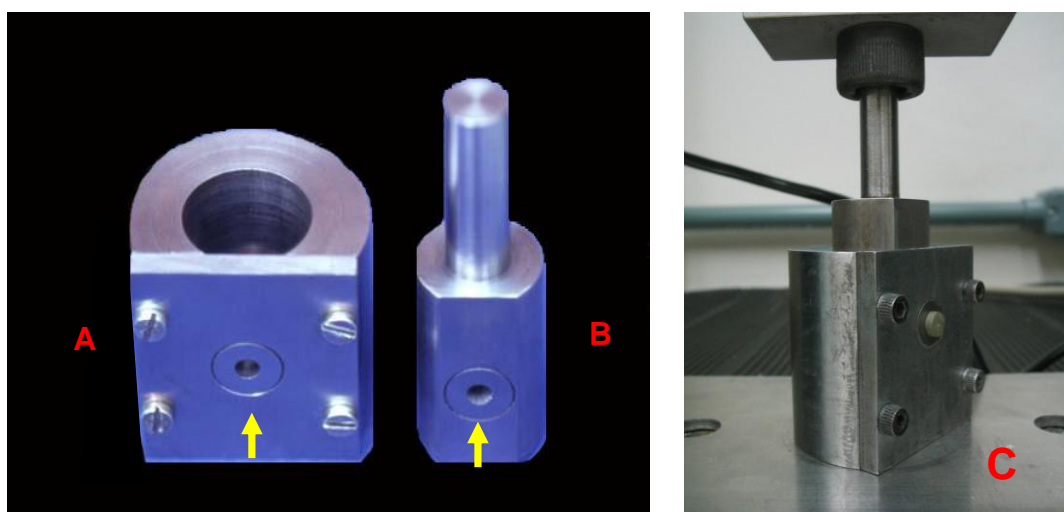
Dispositivo para o ensaio mecânico: a) peça externa; b) peça interna; c) corpo-de-prova posicionado no dispositivo
